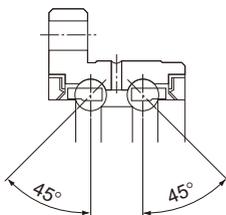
Schnittansicht des Stützlagers beim Typ BNS-A
